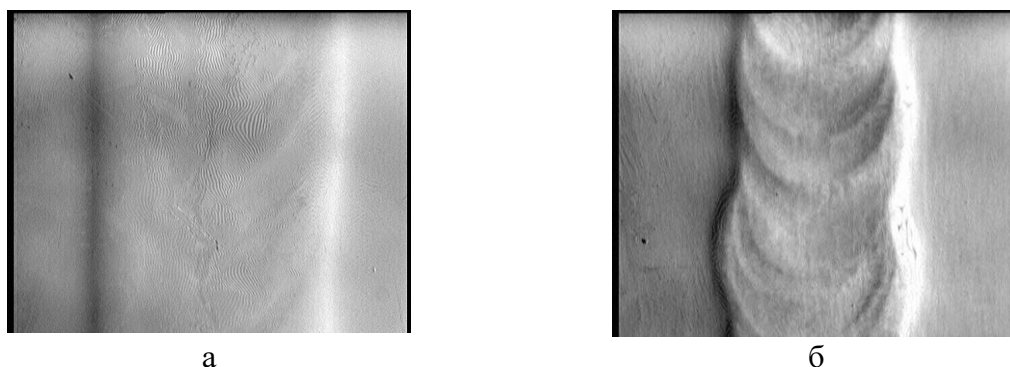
МОВТ образы сварных швов в тестовых образцах из алюминия (а) и нержавеющей стали (б) (увеличение около 10^{\times})
